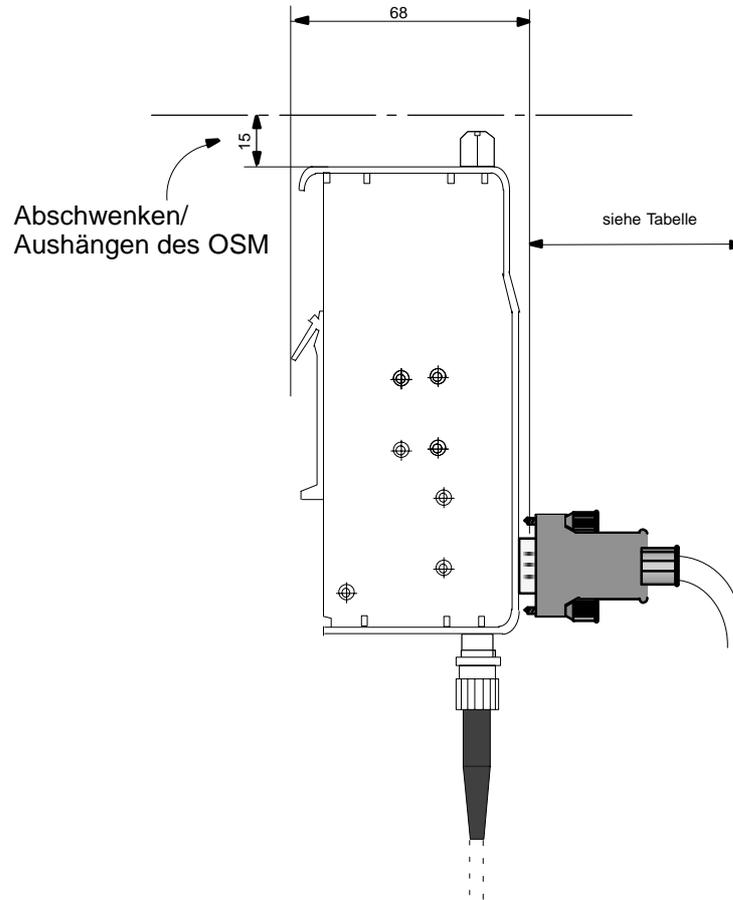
Industrial Ethernet OSM (Seitenansicht; Maße in mm)
